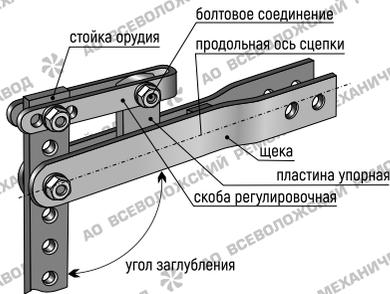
Установка сцепки опорной пластиной вверх (стандартно).
